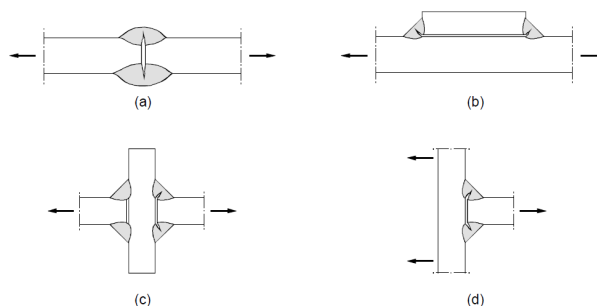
Rotura na raiz da soldadura, adaptado de [21]
